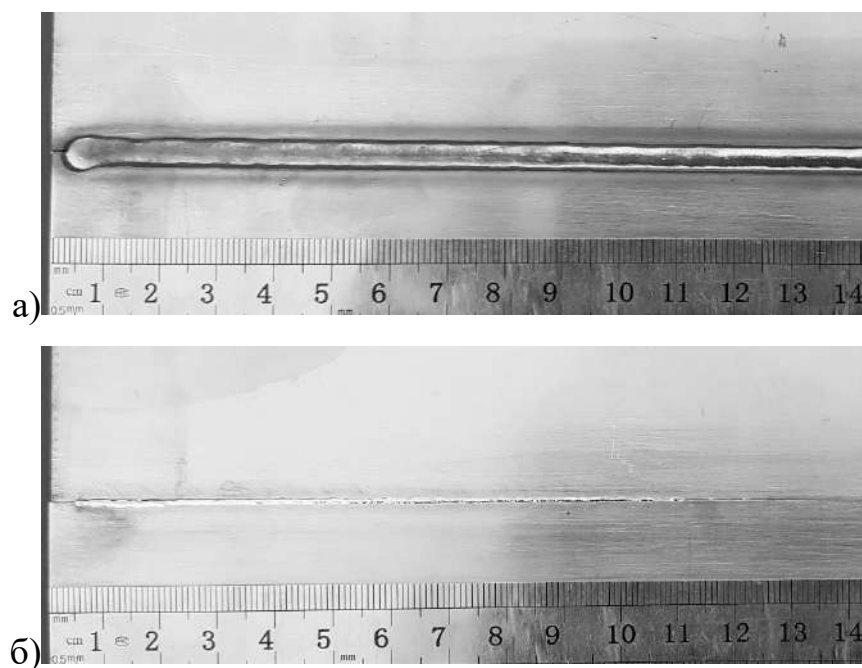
Зовнішній вигляд стикового з'єднання сталі AISI304 $\delta=3,0$ мм: а) – верхня сторона; б) – корінь шва.
